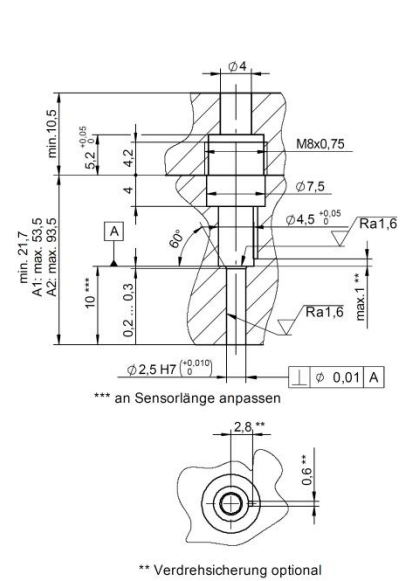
Montagebohrung für Einbau mit ladungsführender Distanzhülse
